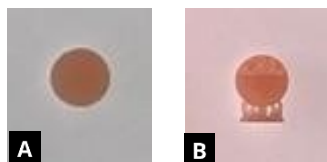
A: Provette impresso a 0° ; B: Provette impresso a 90°
